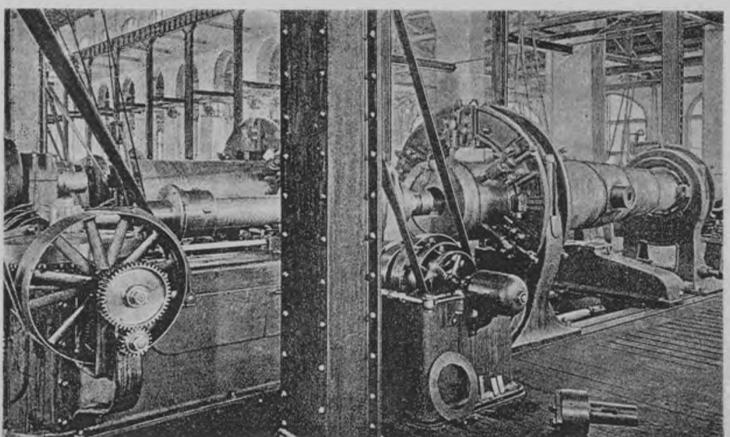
VUE DU TUBE DU CANON DE 305^{m/m} SUR LE TOUR.
